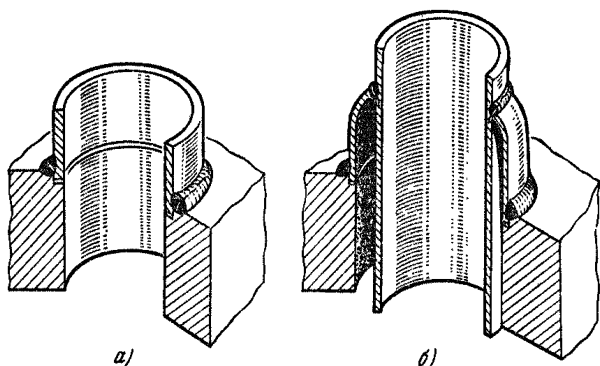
Трещины в сварных швах приварки штуцера к барабану (а) и штуцера с рубашкой (б):
